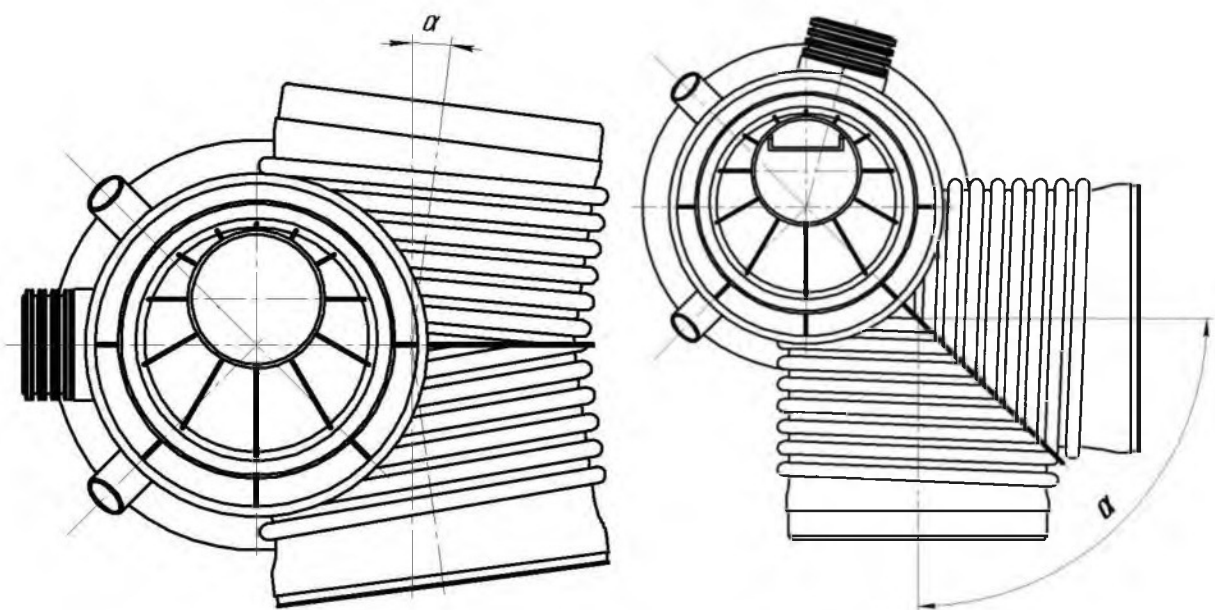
Тангенциальный сварной колодец с отводом
